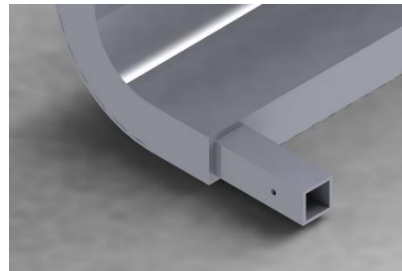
Ensamblaje subconjunto 1. 1. Soldadura 15.
